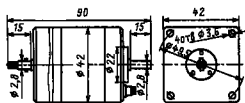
52 Габаритные и установочные размеры двигателей ШДР-50/1800
